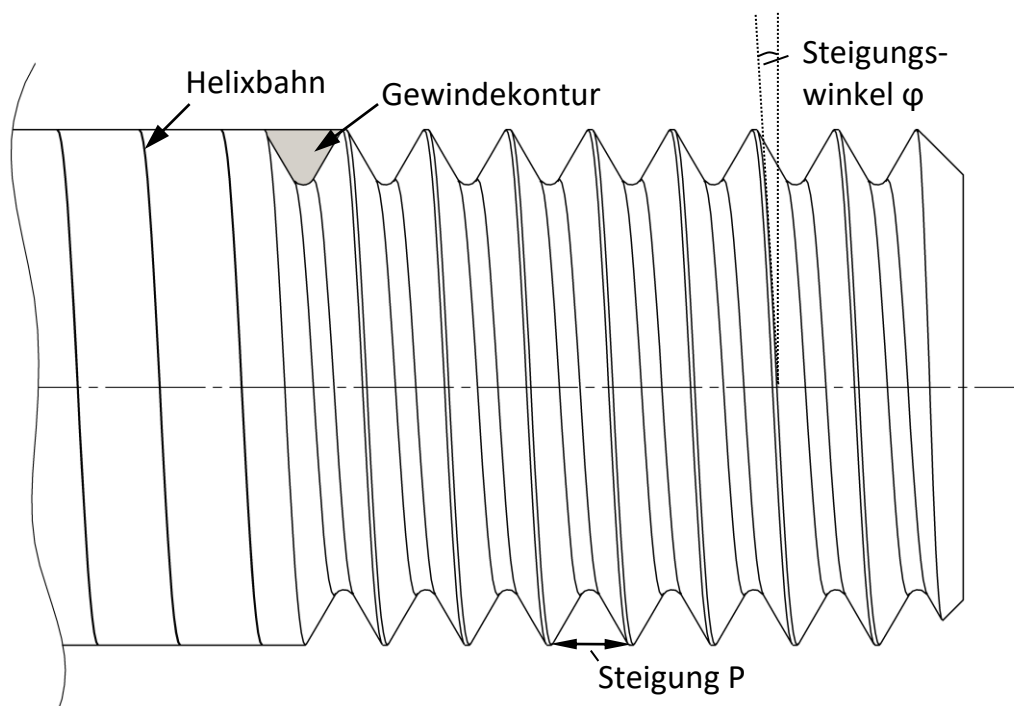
Schraubengewinde als um einen Zylinder gewickelte schiefe Ebene mit Steigungswinkel φ und der Steigung P
